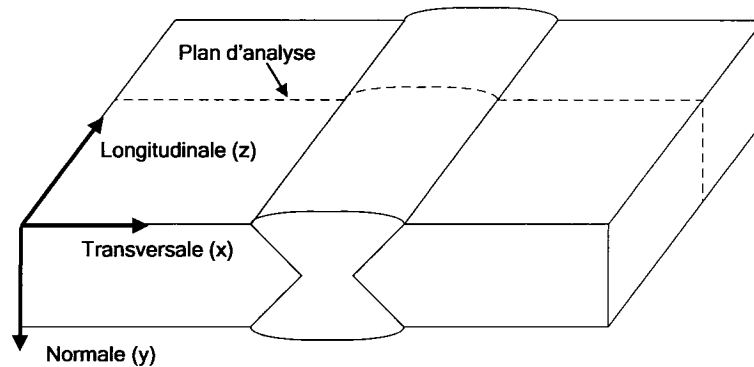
Plaques épaisses soudées bout-à-bout, en double V.
